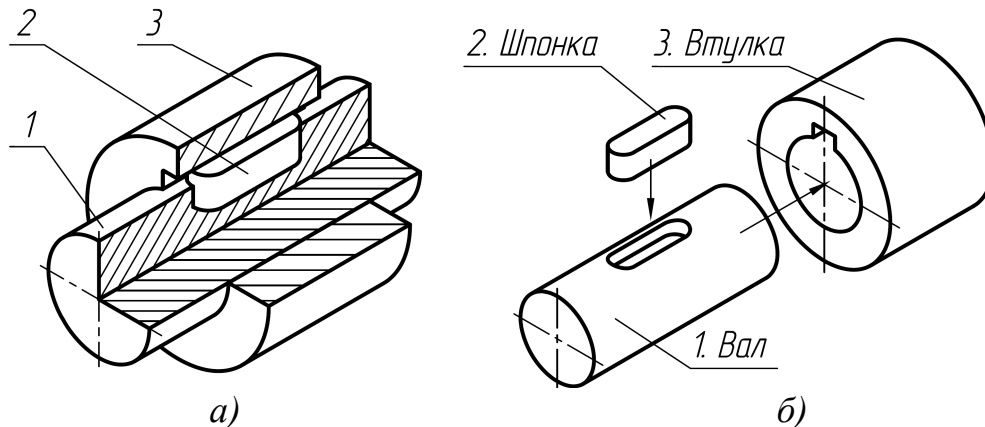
Шпонкове з'єднання: а – загальний вигляд; б – деталі
